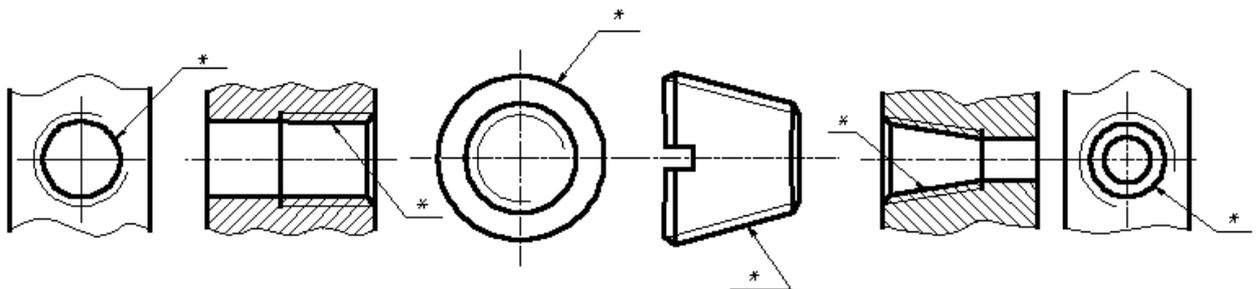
Обозначение трубной цилиндрической и конической резьбы
